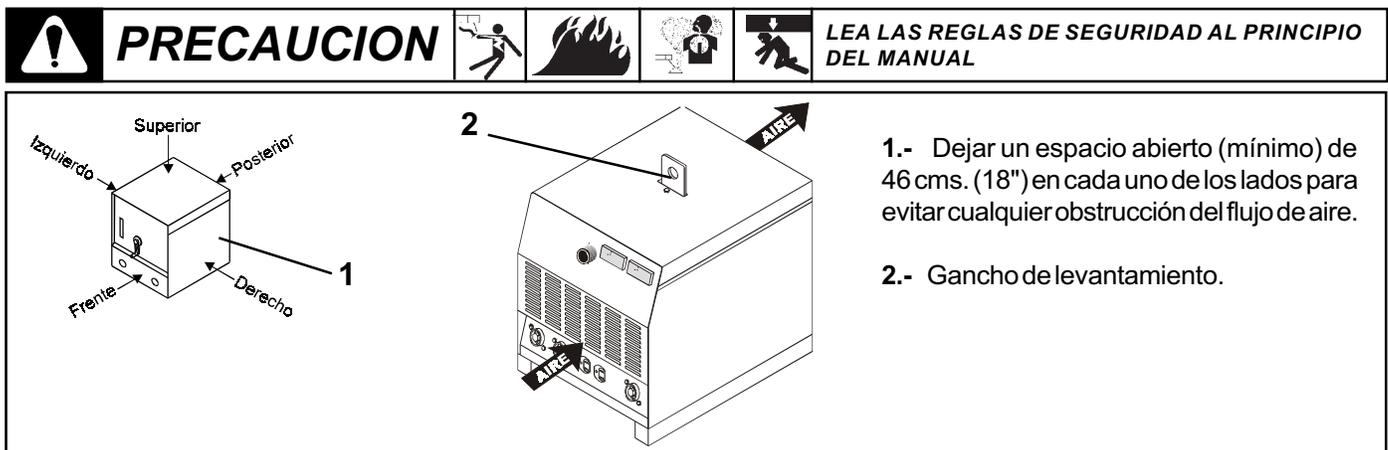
Localización de la Máquina Soldadora.
